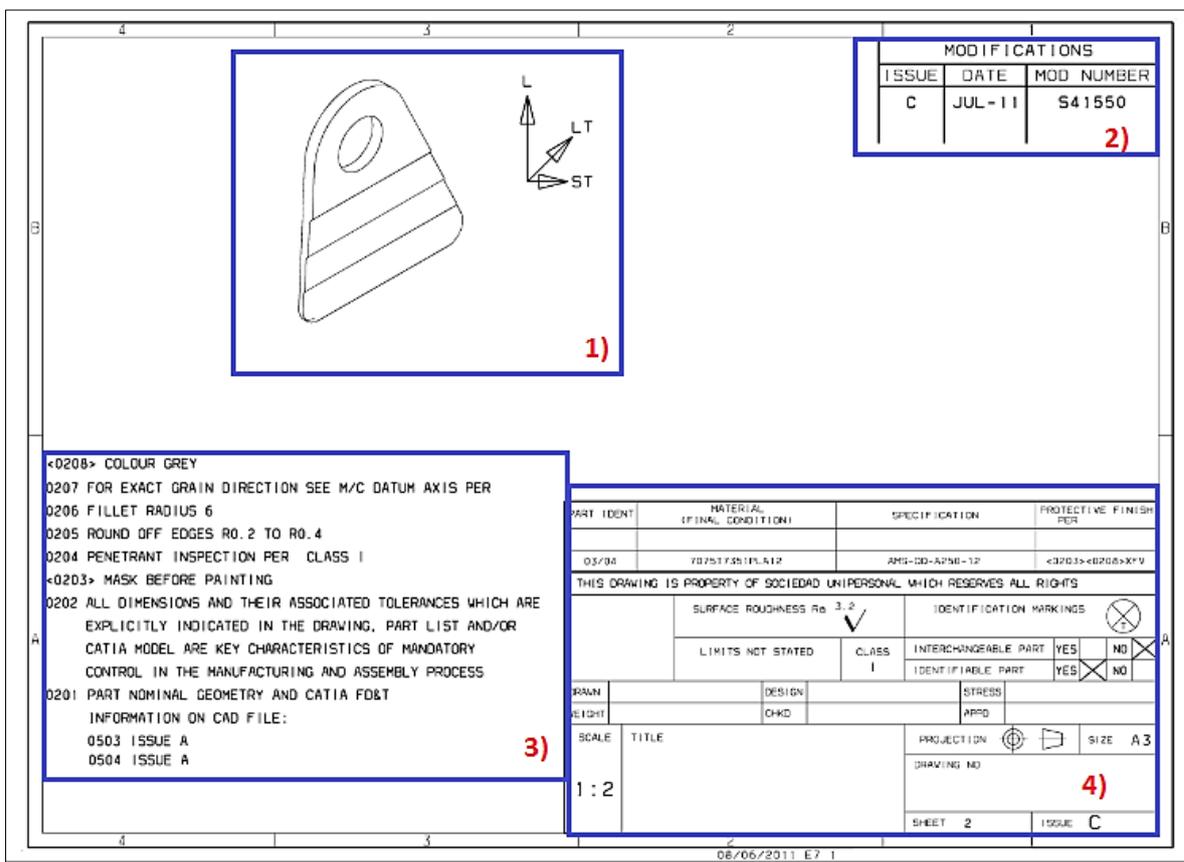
Exemplo de um desenho de um componente aeronáutico. Adaptado de um desenho fornecido pelo cliente.
